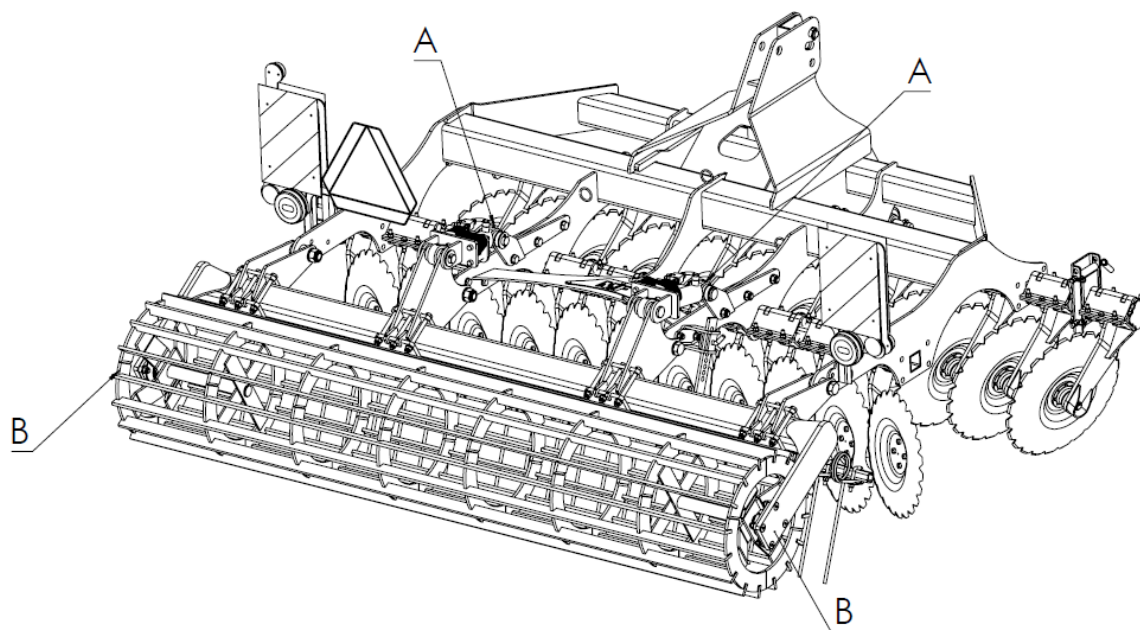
Lubricación de la unidad: A - actuador del eje, B - conjuntos de rodamientos del eje.
